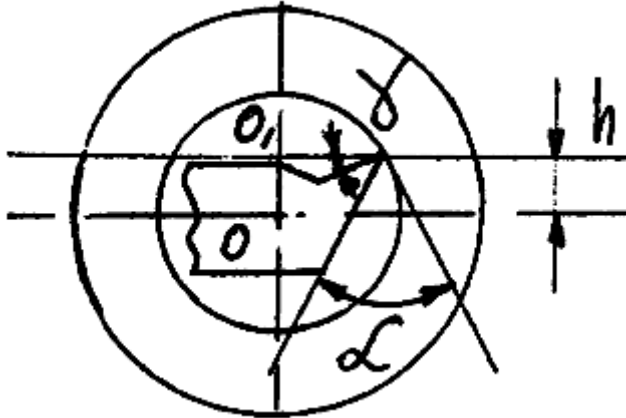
Розміщення вершини різця вище осі обертання заготовки при розточуванні
